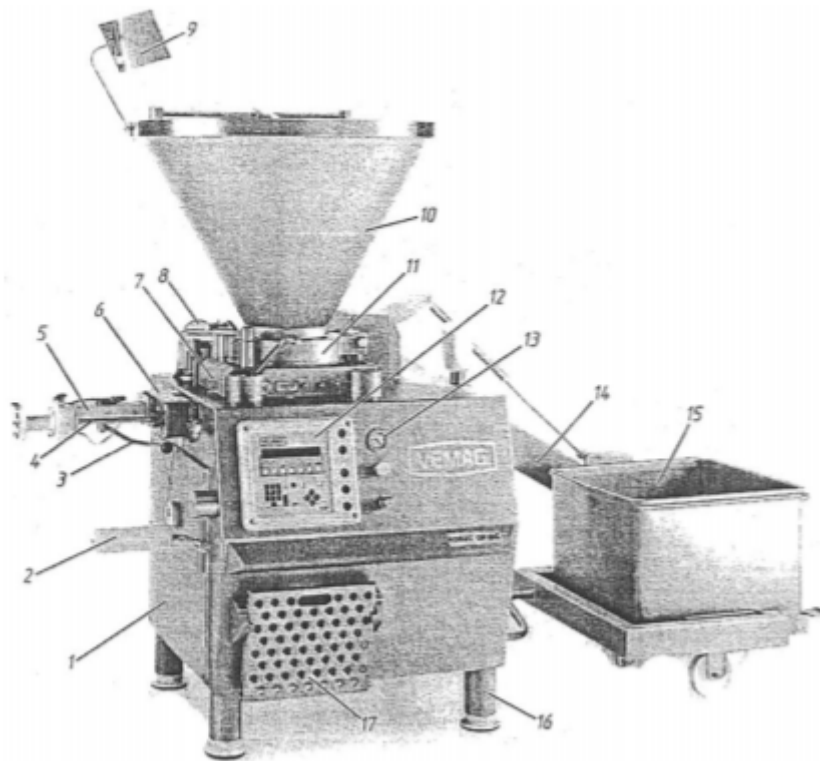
Шприц "Робот ДП-15Ц" фірми "Фемаг" з ексцентриковолопастевим витиснювачем: 1 – корпус; 2 – підколінна педаль; 3 – важіль; 4 – цевка; 5 – підтримуючий механізм; 6 – механізм перекрутки; 7 – корпус витиснювача; 8 – ковпак вакуумної пастки; 9 – дзеркало; 10 – бункер; 11 – корпус приводу спіралі, яка подає фарш; 12 – пульт керування; 13 – вакуумметр; 14 – підйомник-перекидач; 15 – візок; 16 – опора; 17 – відкидна площадка
